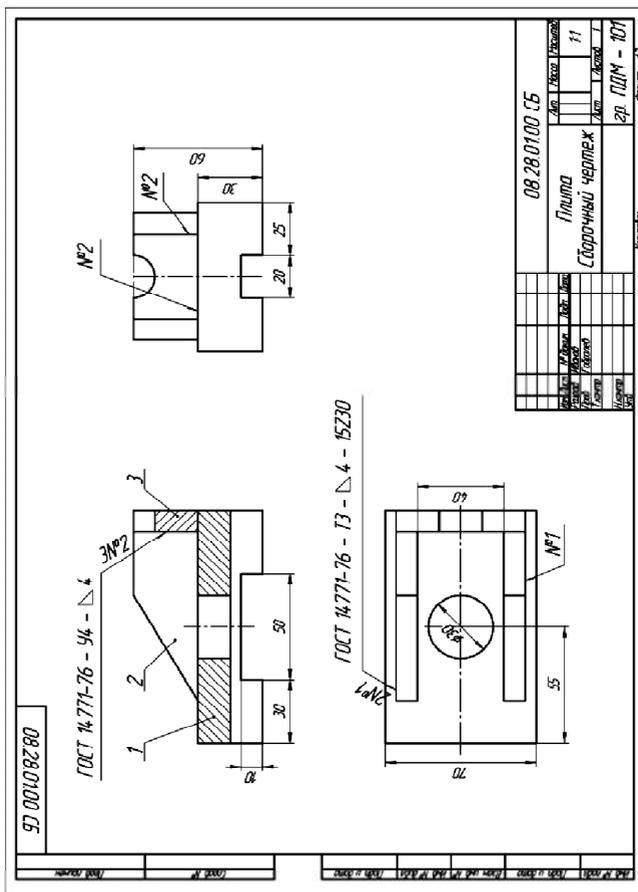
Пример выполнения сборочного чертежа сварного изделия
